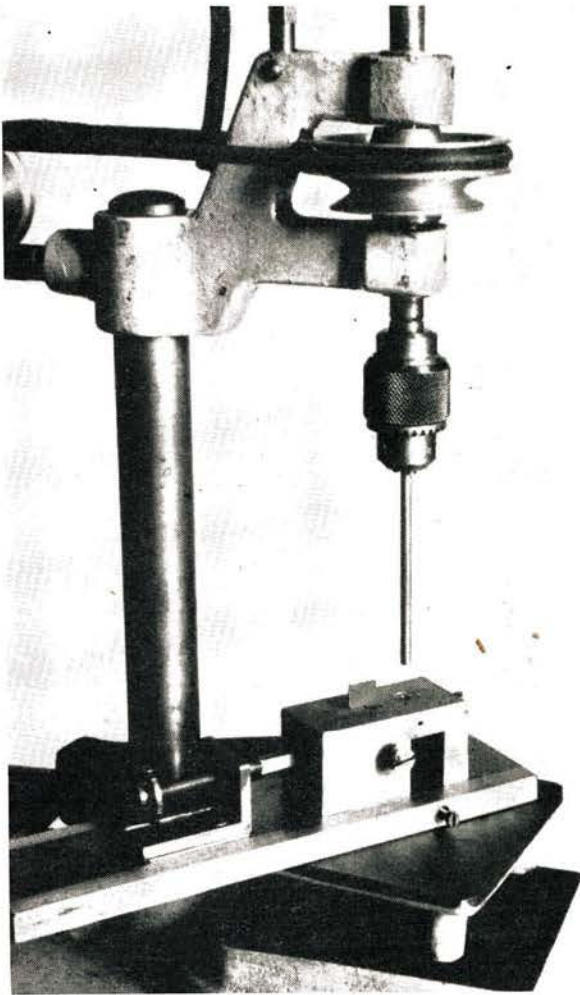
Die Drehvorrichtung auf dem Bohrmaschinentisch. In dem Bohrfutter ist das eingespannte Werkstück zu erkennen.
